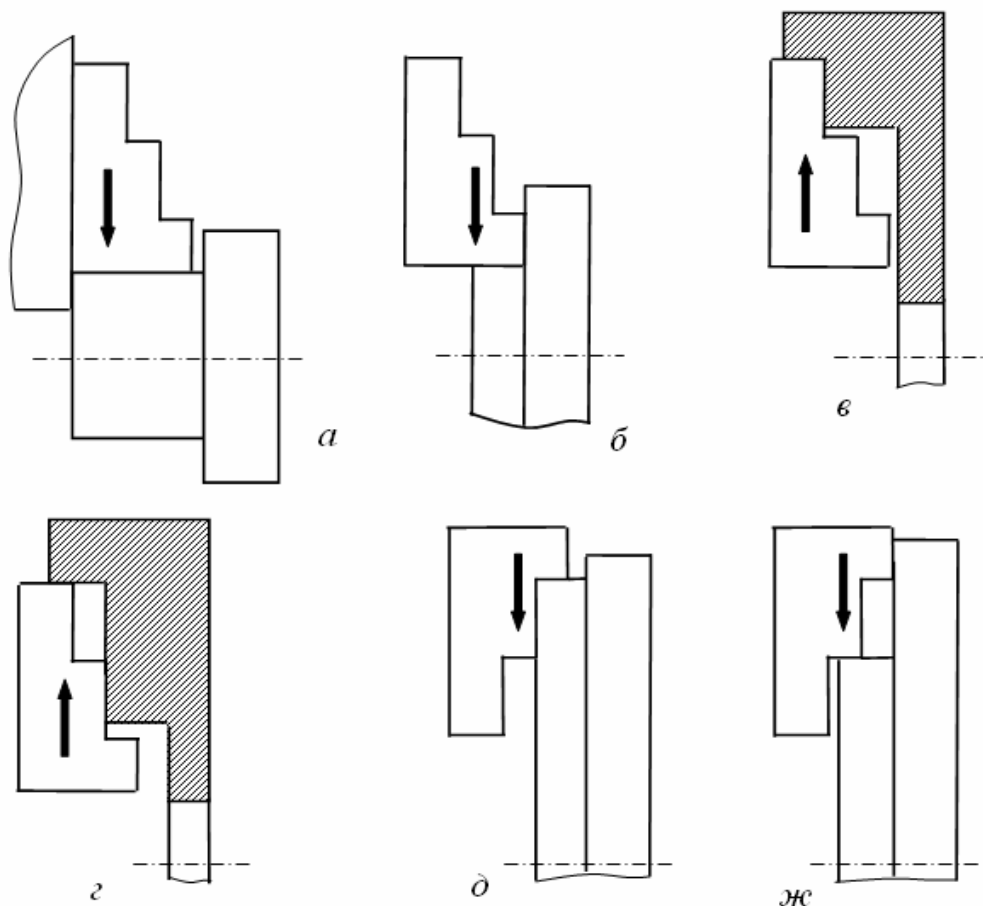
Варіанти встановлення заготовок деталей типу «Фланець» у трикулачковий самоцентрувальний патрон
